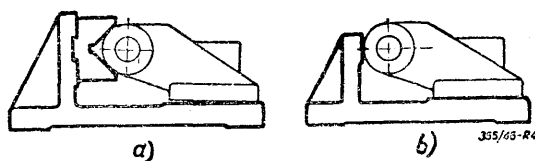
i 4 przedstawiają kilka przykładów błędnego i właściwego wyboru podstaw obróbkowych
